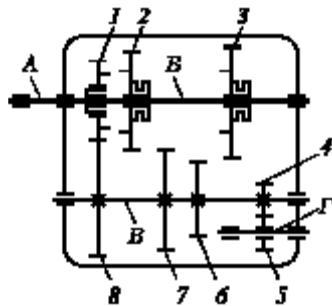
Схема тріступінчастої коробки передач: А – ведучий вал; В – ведений вал; Г – проміжний вал; Г – вісь зубчастого колеса передачі заднього ходу; 1-8 – зубчасті колеса
